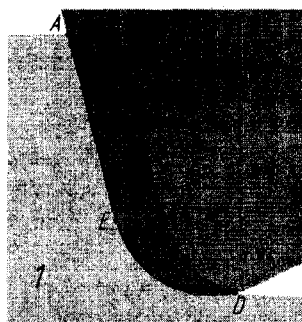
Схема зоны контакта режущей части инструмента с заготовкой при врезании:
